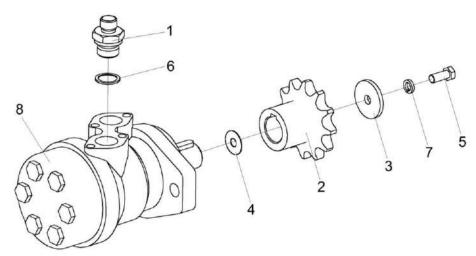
Гидромотор заточного устройства КВС-2-0116680-01
